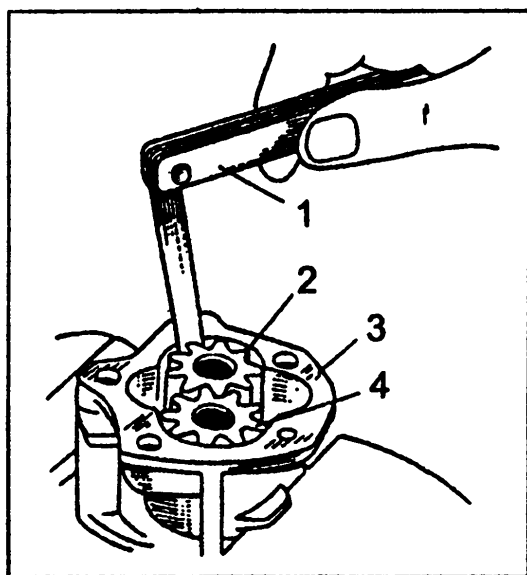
Измерение зазора между корпусом насоса и зубьями шестерен (насос с наружным зацеплением шестерен):
